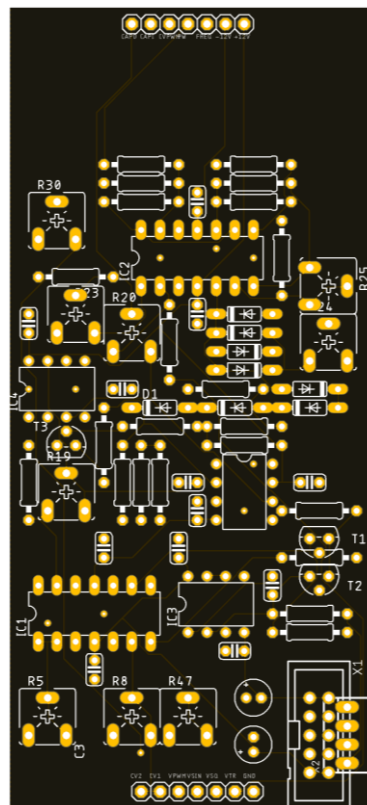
Board Layout: Pots&Sockets PCB
